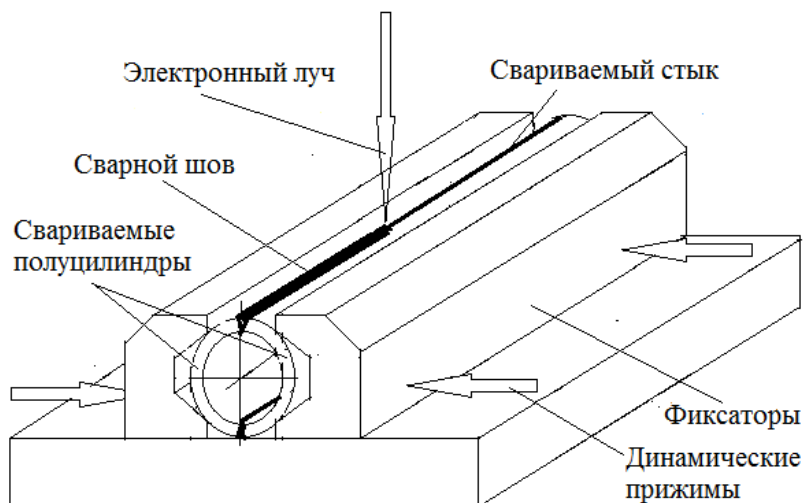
Оснастка для сварки монокристаллического цилиндрического катода из двух полуцилиндров
